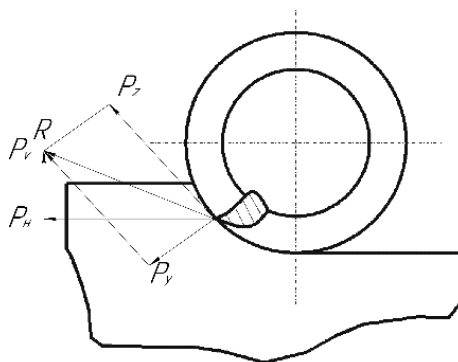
Схема сил при обработке цилиндрической прямозубой фрезой
